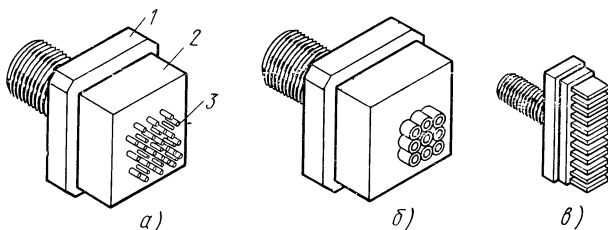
Групповые инструменты для обработки отверстий и пазов:
